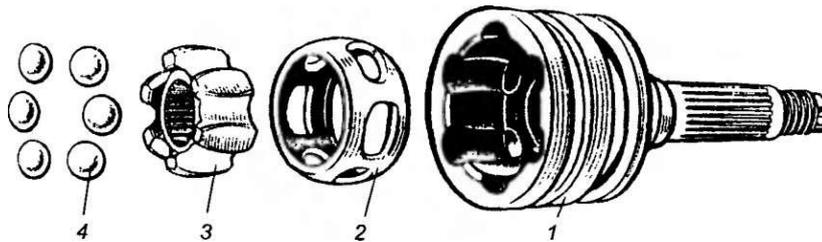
Детали наружного шарнира привода передних колес: 1 — корпус шарнира; 2 — сепаратор; 3- ; 4 — шарики
